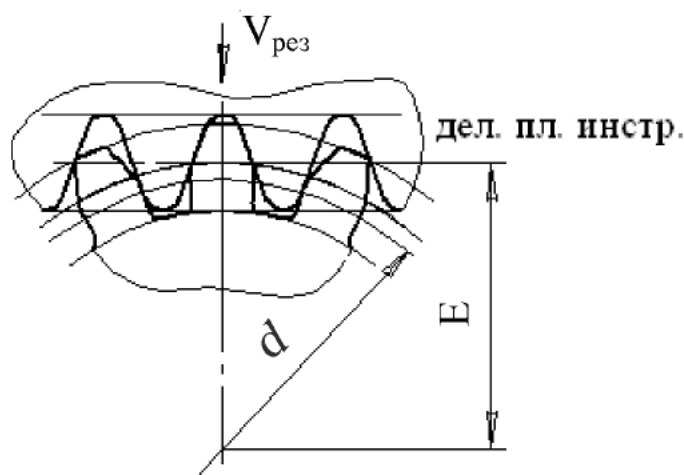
Схема нарезания зубчатого колеса со смещением
